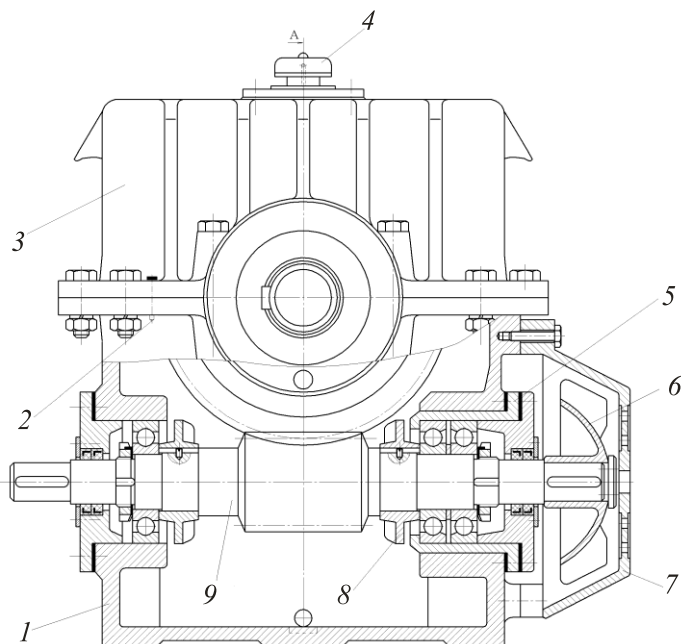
Редуктор червячный одноступенчатый с вентилятором (вид спереди)
